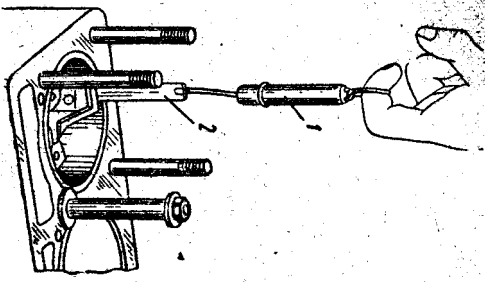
Приспособление для съема гильзы цилиндра из блока.
